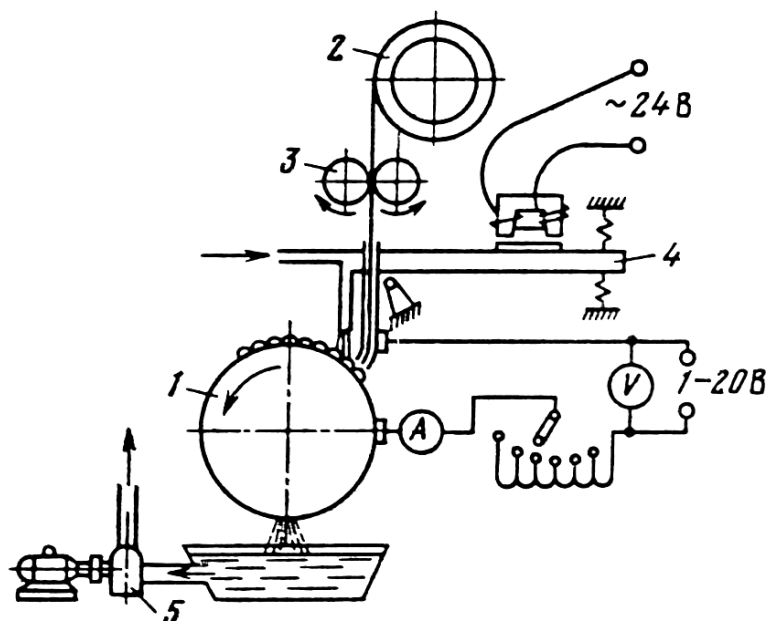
Схема установки для вибродуговой наплавки деталей:
